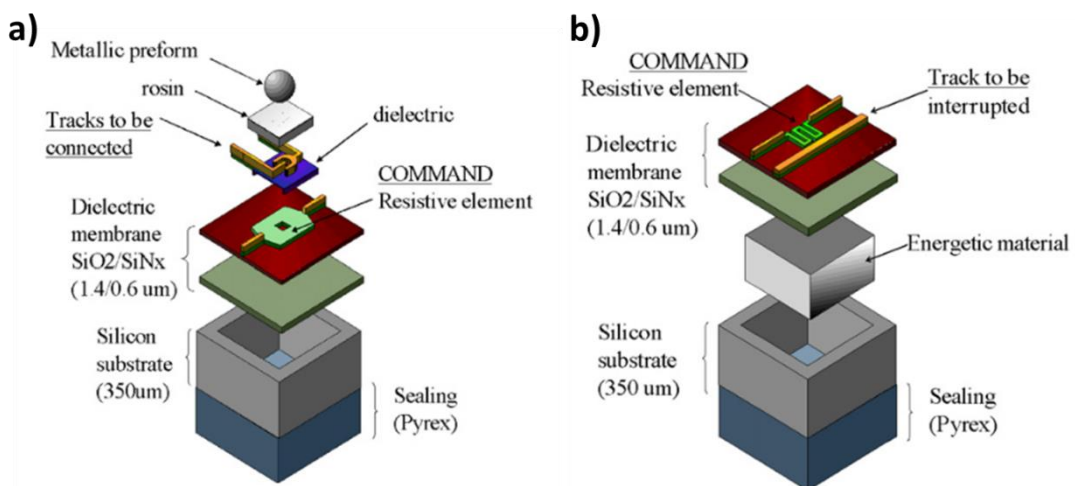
vue explosée des deux switches pyrotechniques réalisés par P. Pennarun : (a) OFF -> ON, (b) ON -> OFF [80]
